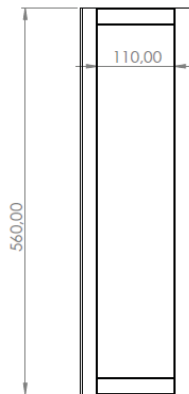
Креслення рамки для встановлення передніх коліс
